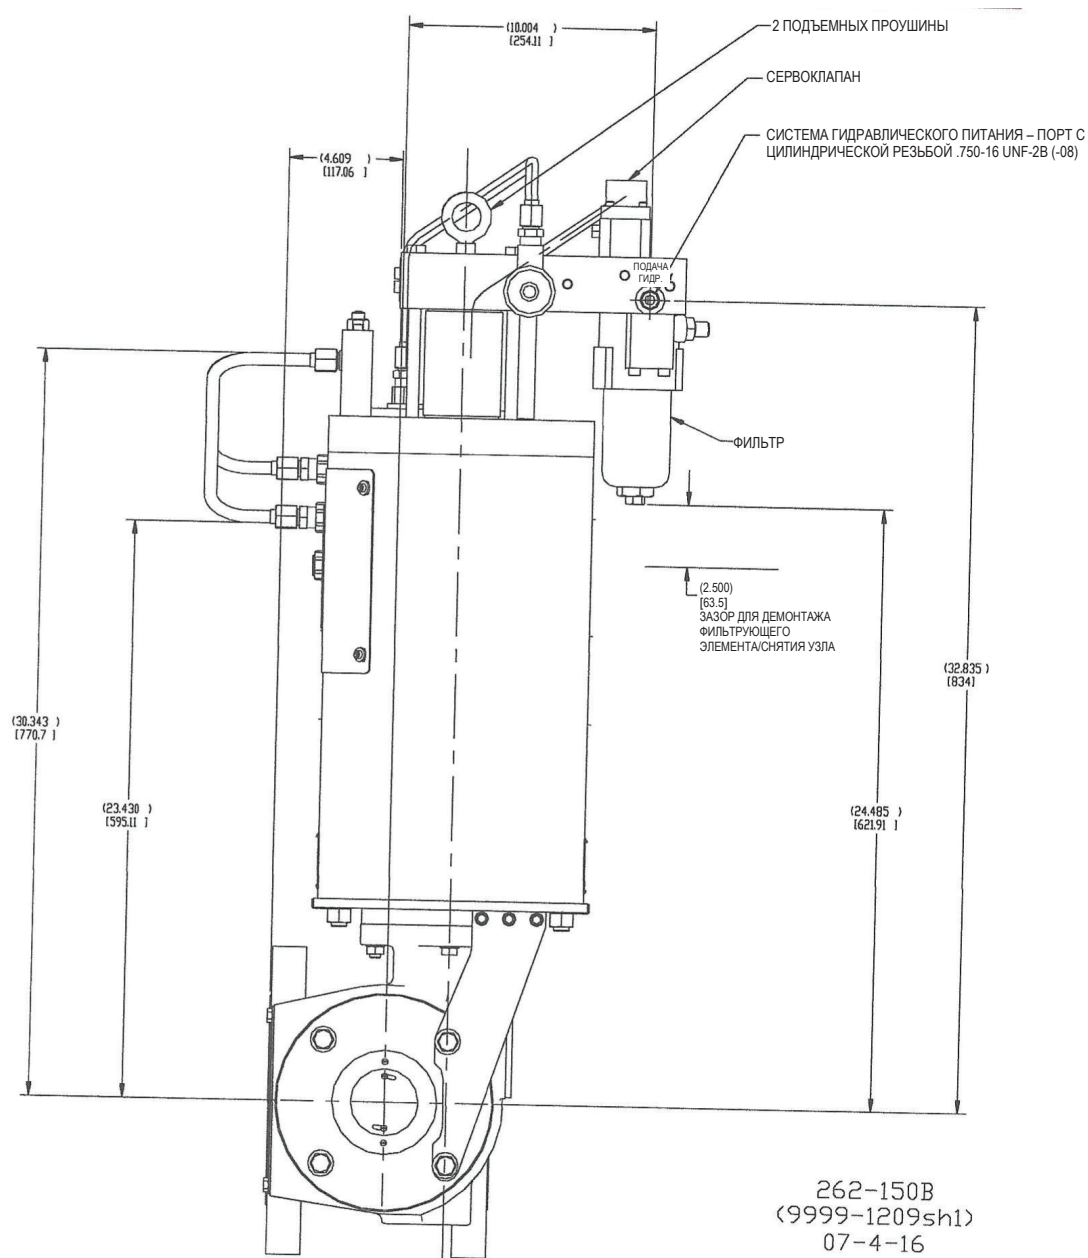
Габаритный чертеж 6" запорно-регулирующего газового клапана (SS260)
